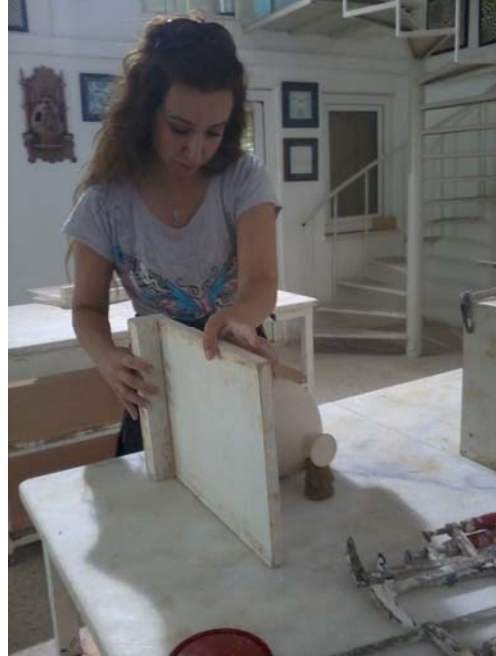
Alçı tornasında şekillendirilen formun su zımparası ile düzeltilmesi
